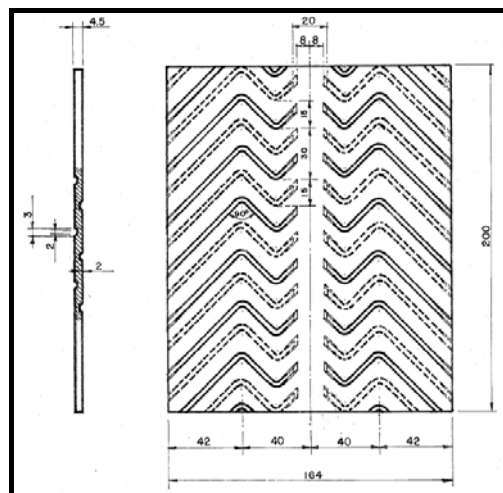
Placa de asiento de caucho. Fuente: NRV3210.
